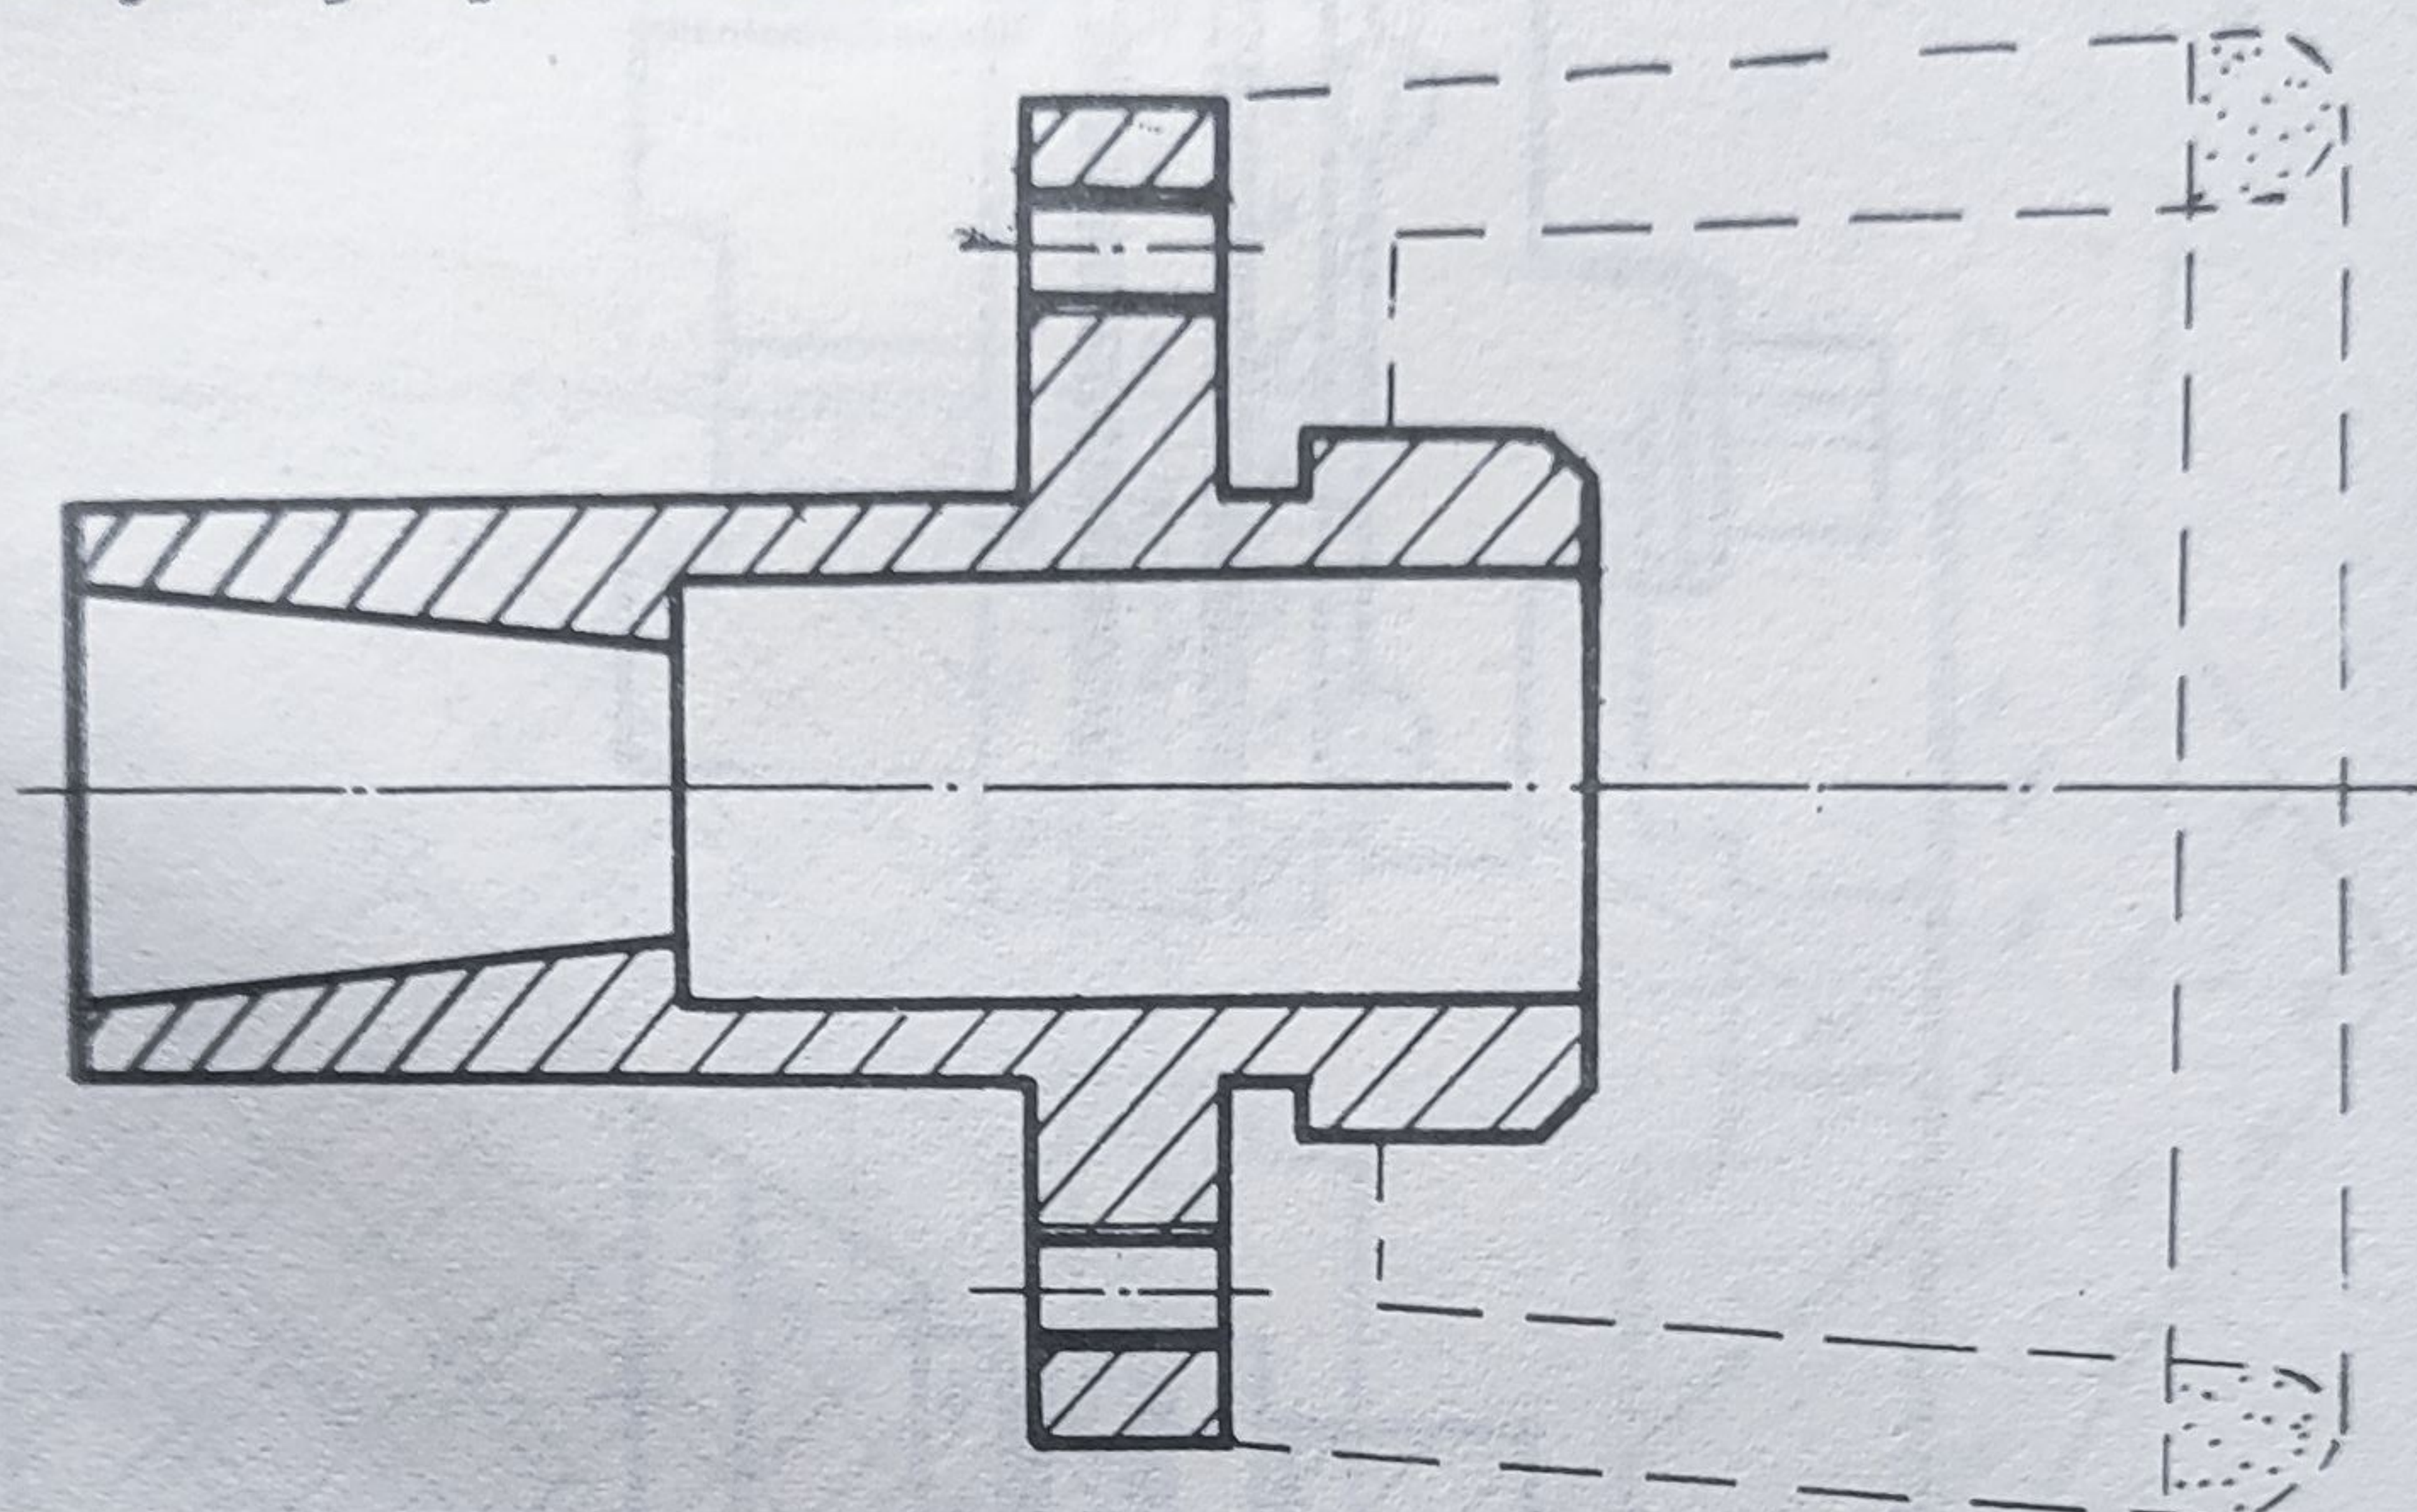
Mufă pentru prinderea frezei tip oală.
